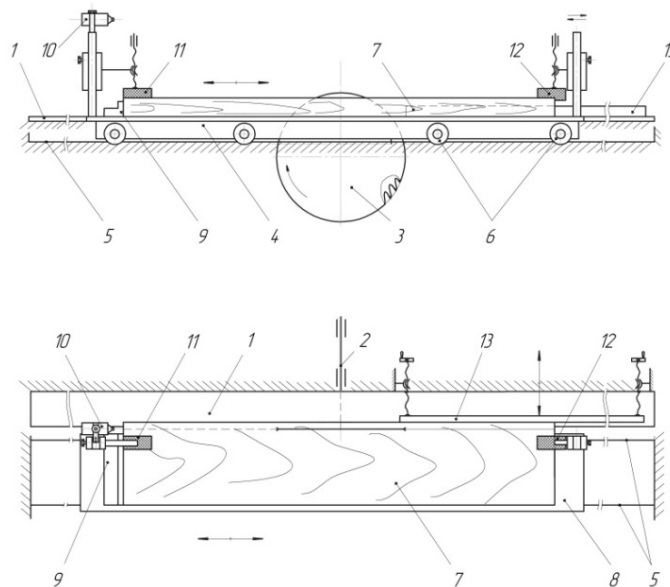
Принципова схема круглопилкового верстата для поздовжнього розпилювання дощок, 1 – боковий підтримуючий стіл; 2 – пилковий вал; 3 – кругла пилка; 4 – каретка; 5 – напрямники; 6 – ролики; 7 – заготовка; 8 – робоча поверхня каретки; 9 – лівий торцевий упор; 10 – лазерний вказівник; 11 – вертикальний притискач; 12 – правий рухомий притискач; 13 – упорна лінійка
